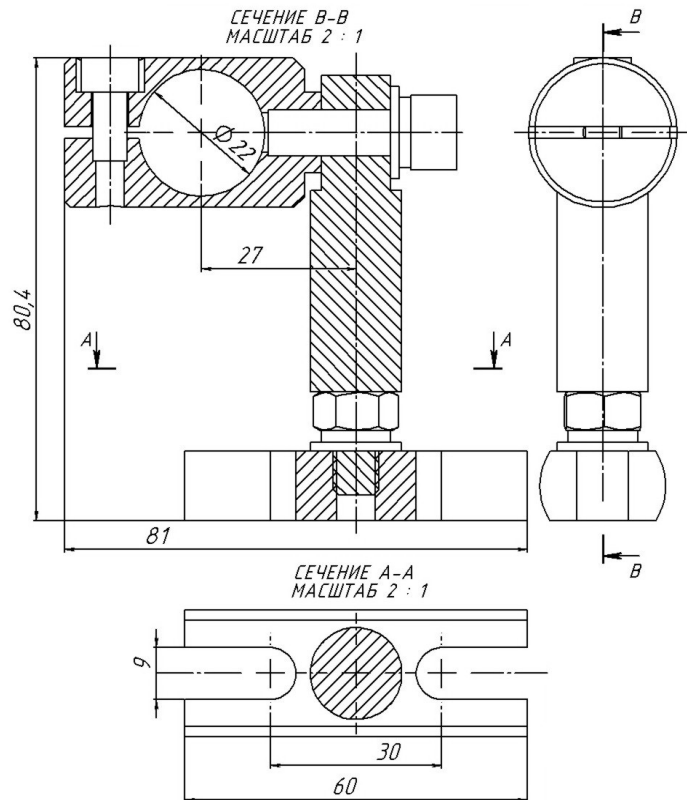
Габаритные и установочные размеры стойки Тип А.
